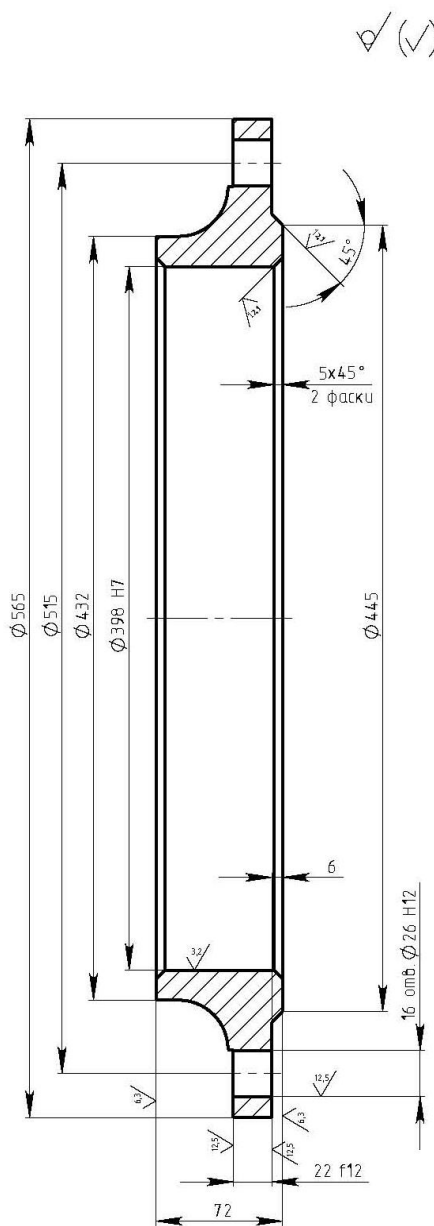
Креслення деталі для вибору способу отримання заготовки
